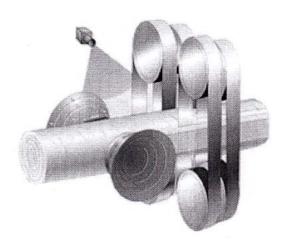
Схема использования ленточнопильного станка с фрезерно-брусующим модулем
